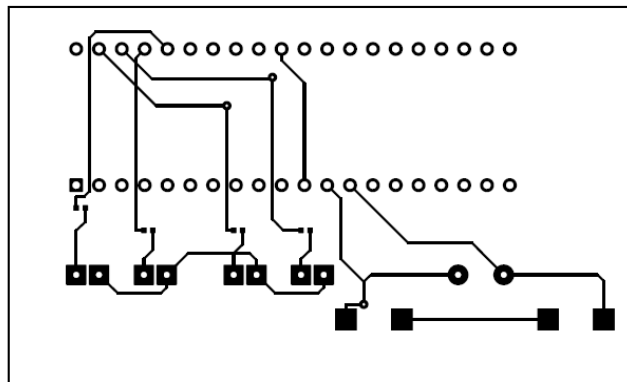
Layout PCB impresso [Elaborada Pelos Autores]
